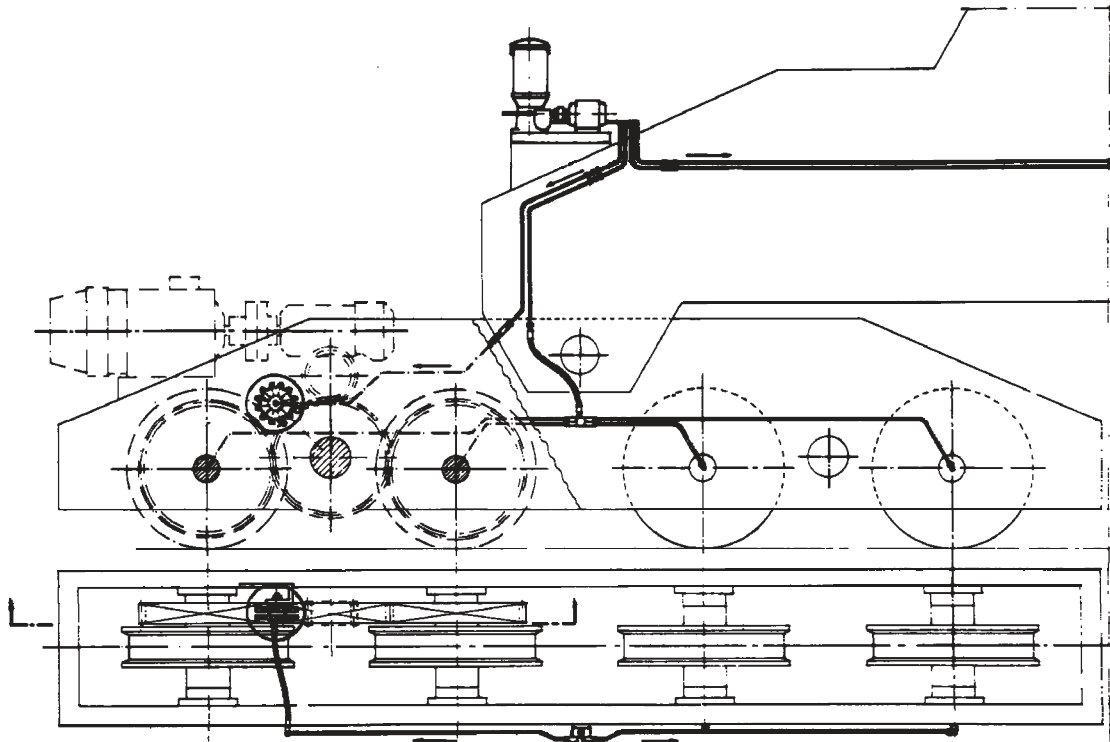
Смазка ведущей и ведомой шестерни на одноковшовом экскаваторе (роторном экскаваторе для выгрузки)
